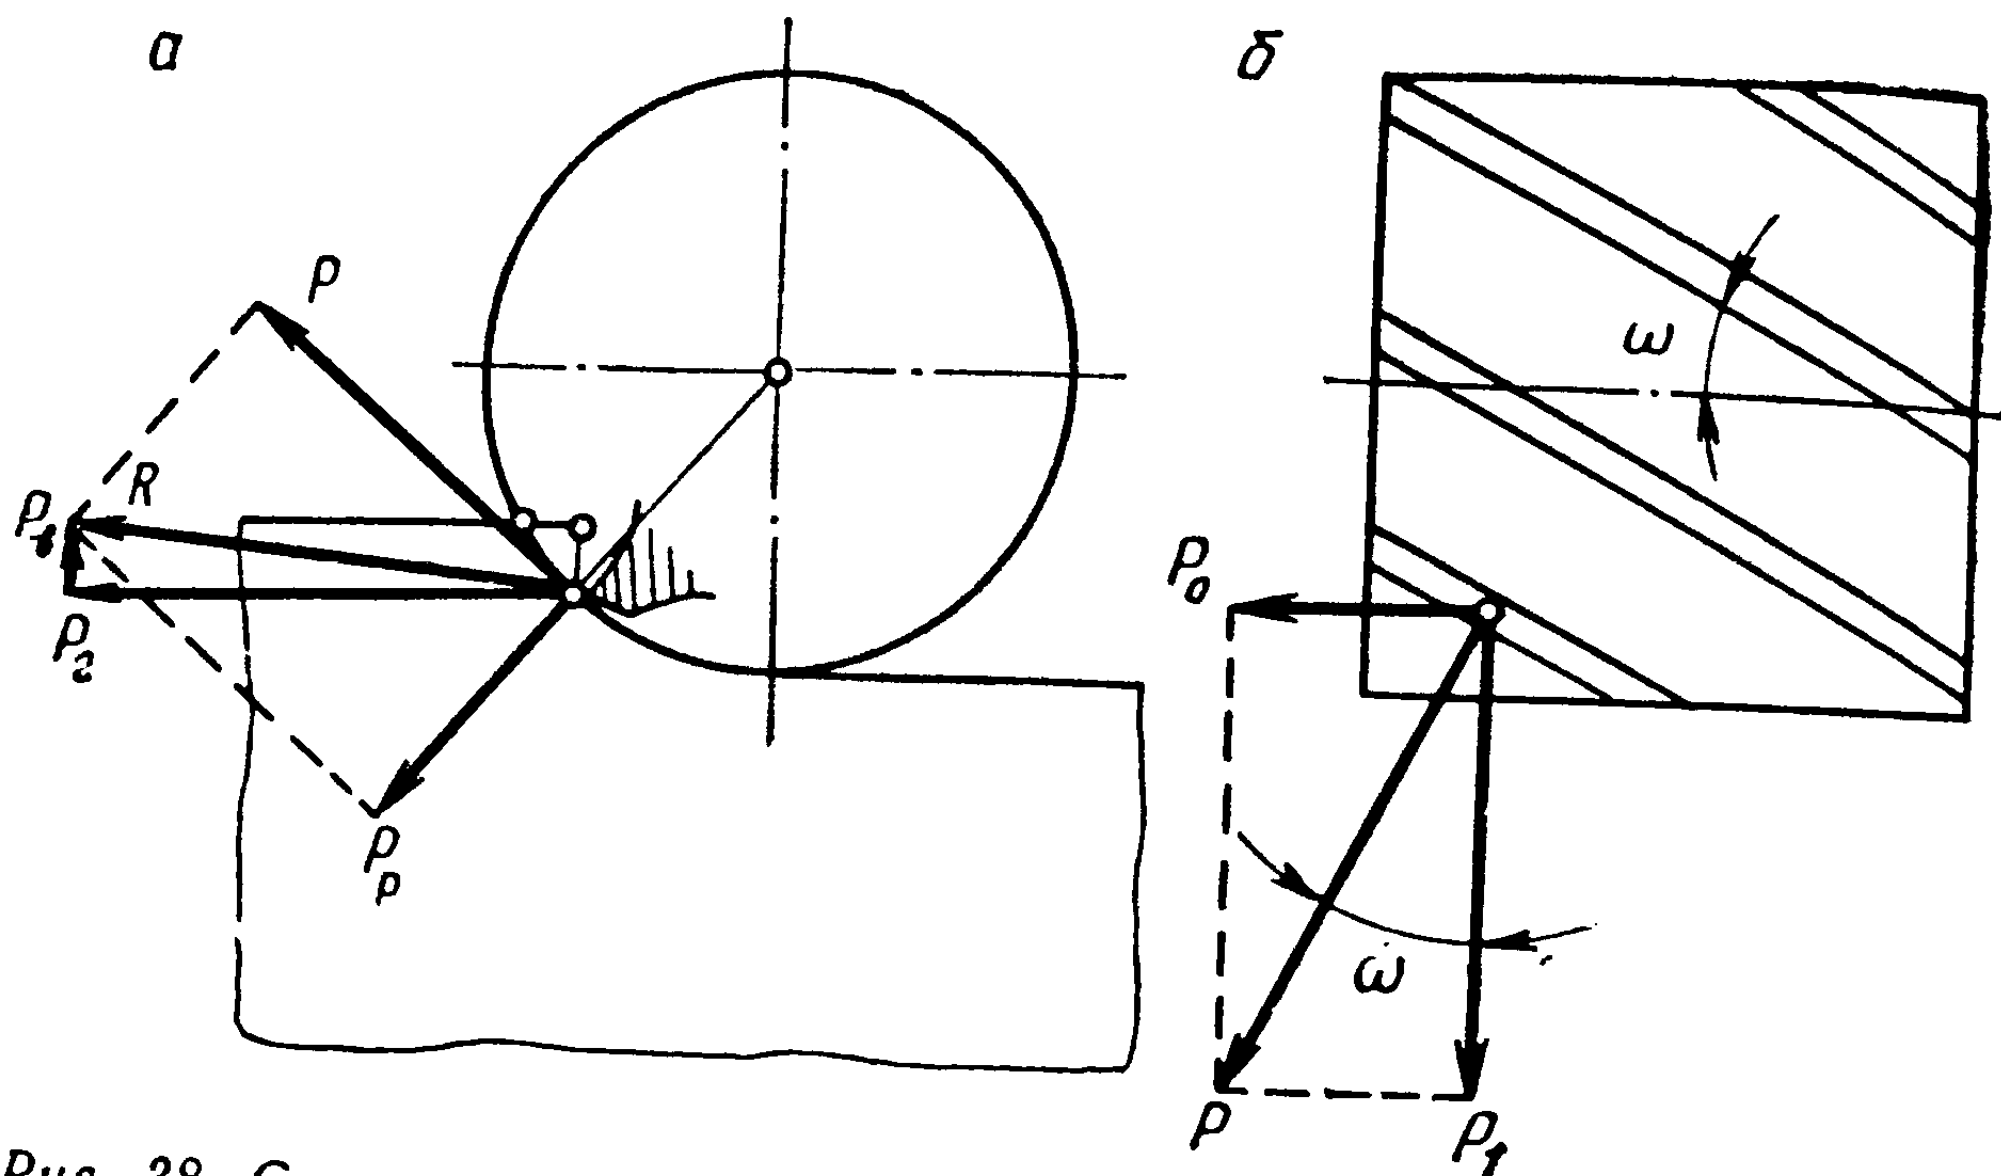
Схема сил, действующих при фрезеровании цилиндрической фрезой с винтовыми зубьями методом против подачи.
